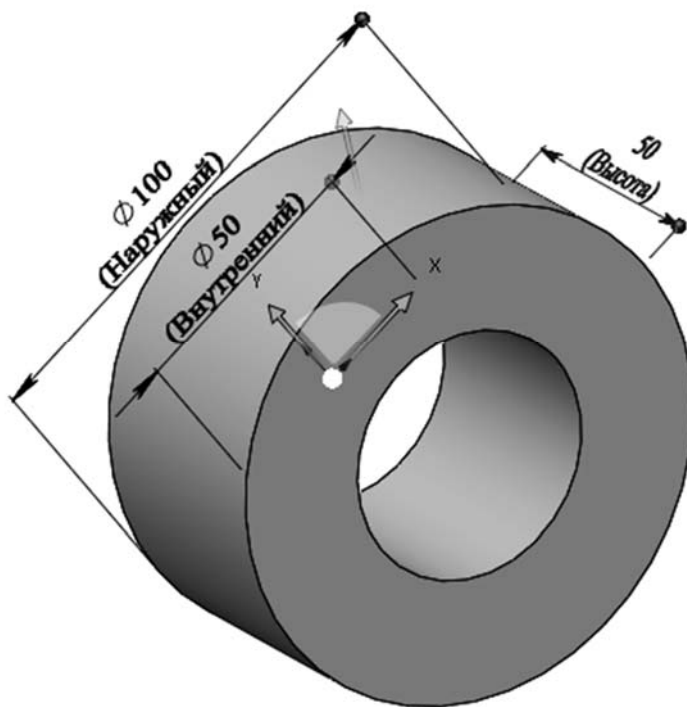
Изображение меню для настройки отображения размеров, детали, свойства размера
